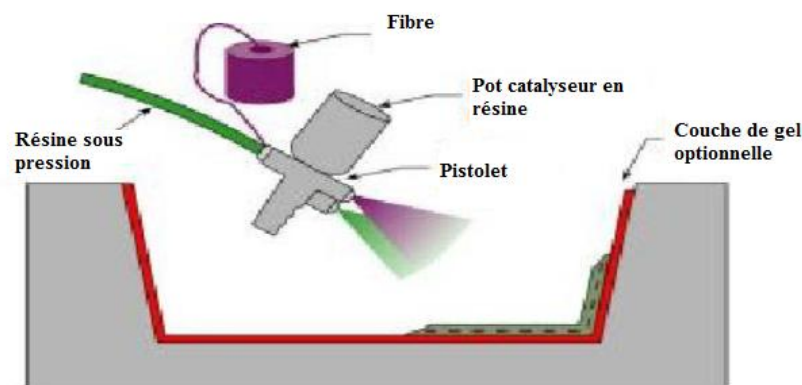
Techniques de moulage ouvert pose au pistolet [203].
